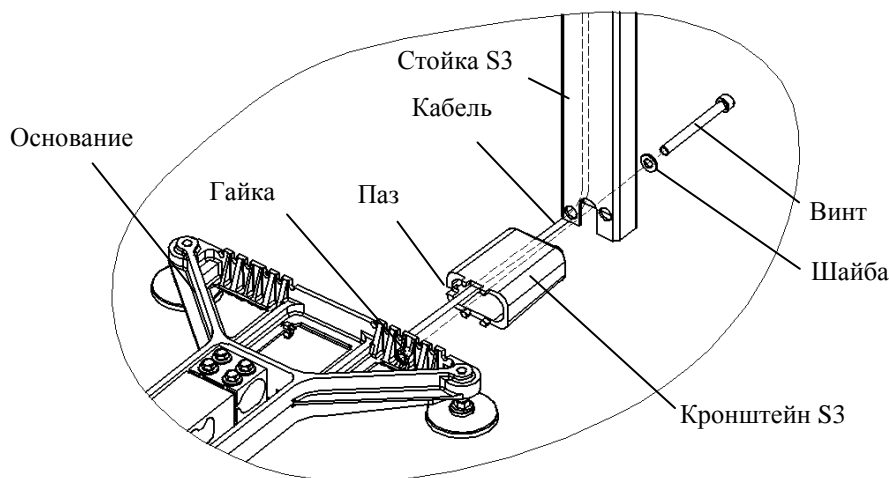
Крепление прямоугольной стойки к основанию весовой платформы
